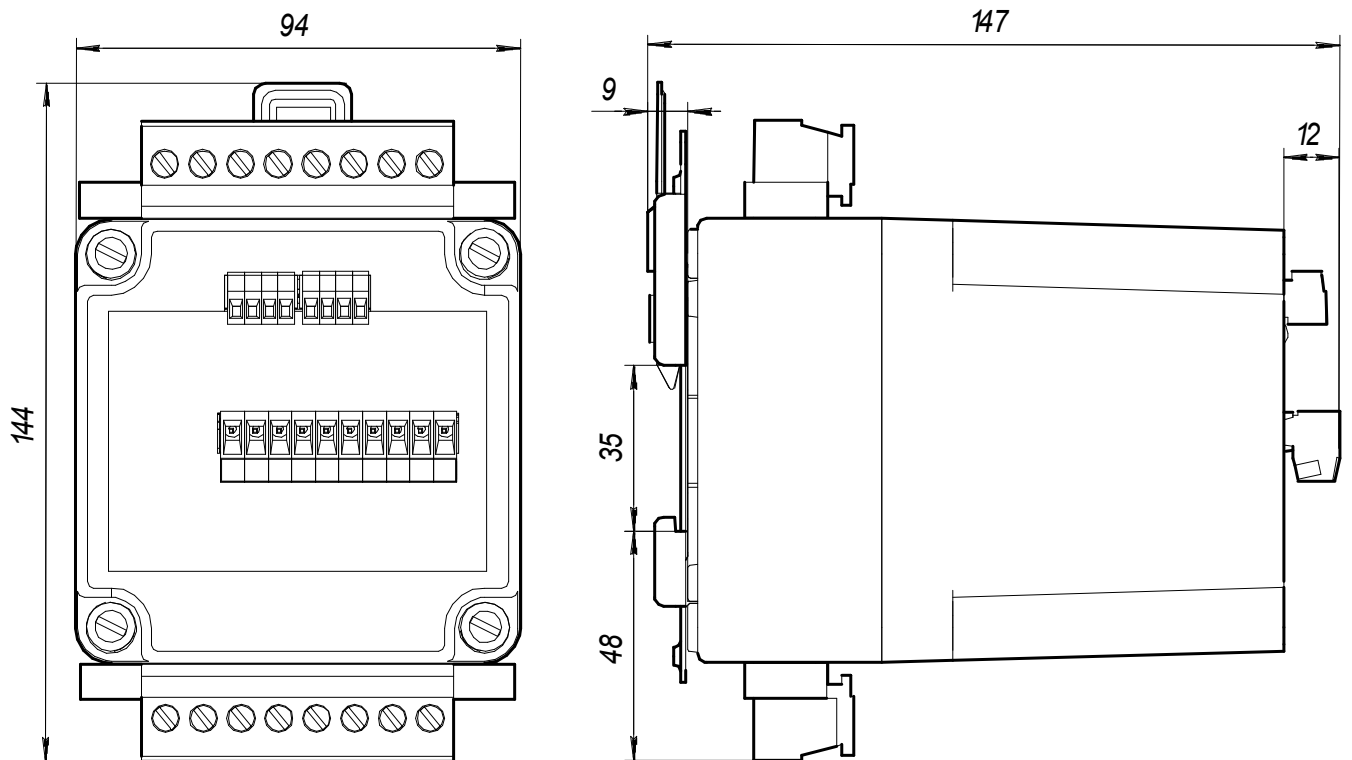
Габаритные и присоединительные размеры ПИ849Ц/XX-1 и ПИ849Ц/XX-2 с креплением на DIN -рейку
